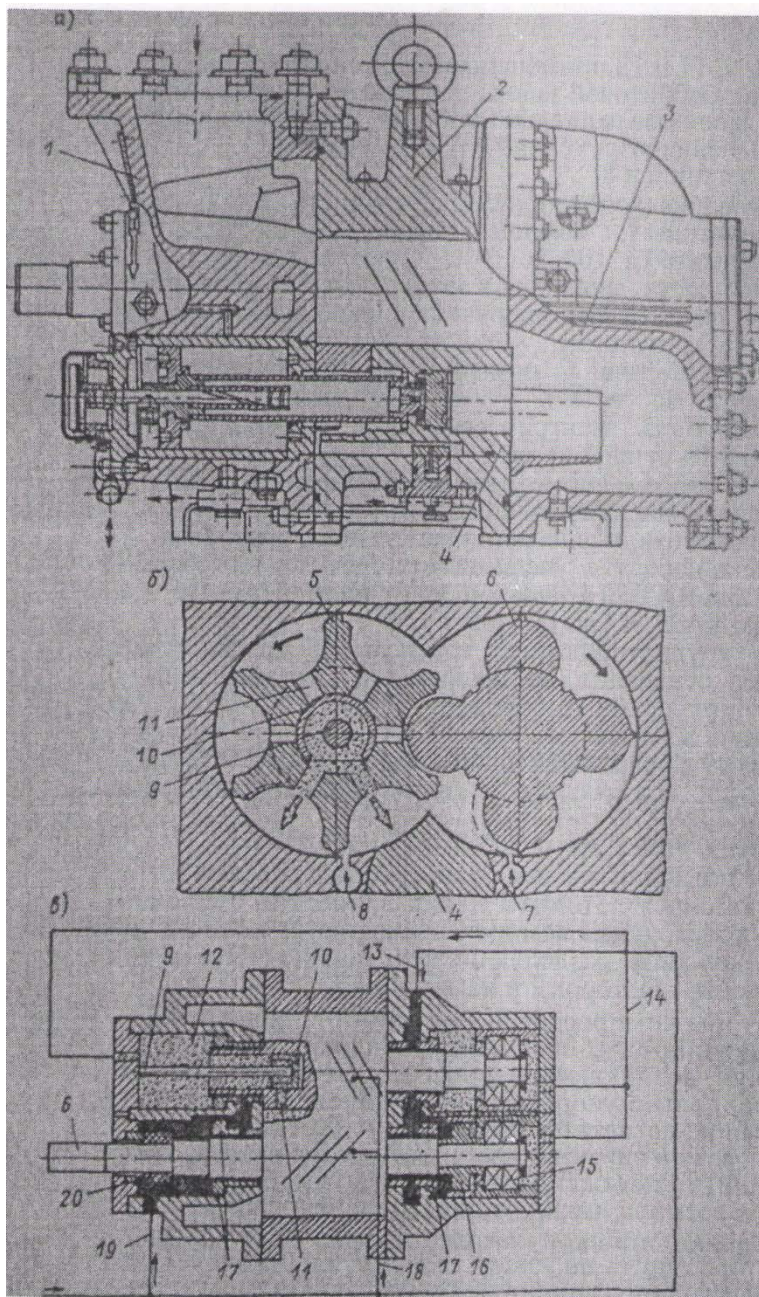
Компрессор типа S3-900: а — продольный разрез; б — расположение окна всасывания и масляного золотника; а — схема подачи масла в компрессор
